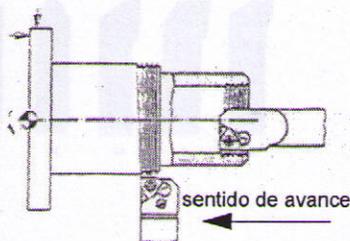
Rosca derecha en giro derecho del husillo de máquina
